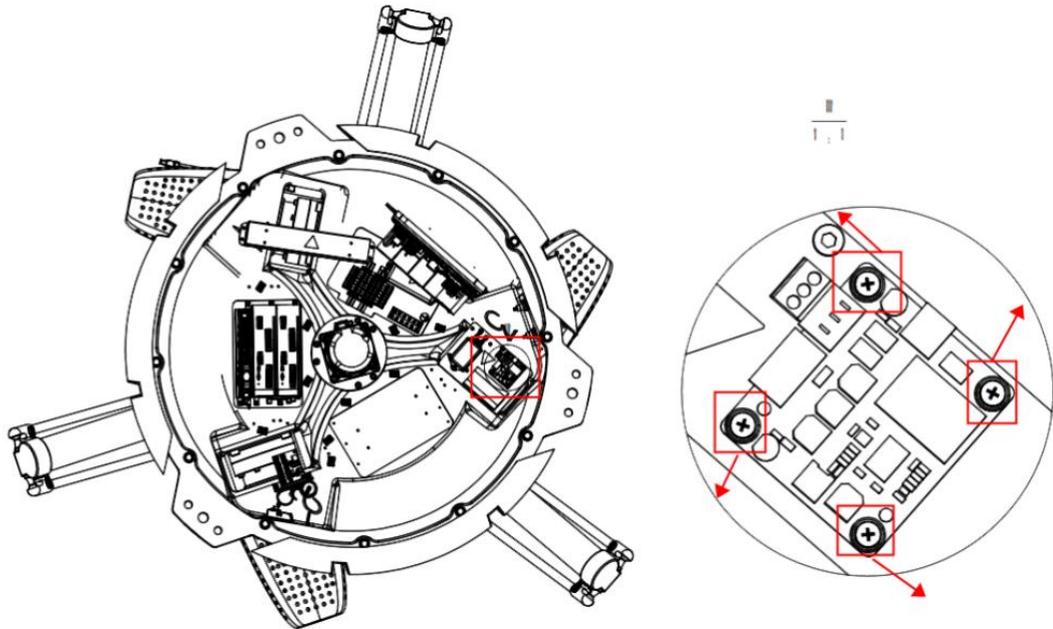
拆卸 UPS 电源 PCBA 固定螺钉
